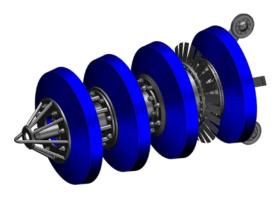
Общий вид устройства калибровочного типа ВКУ
